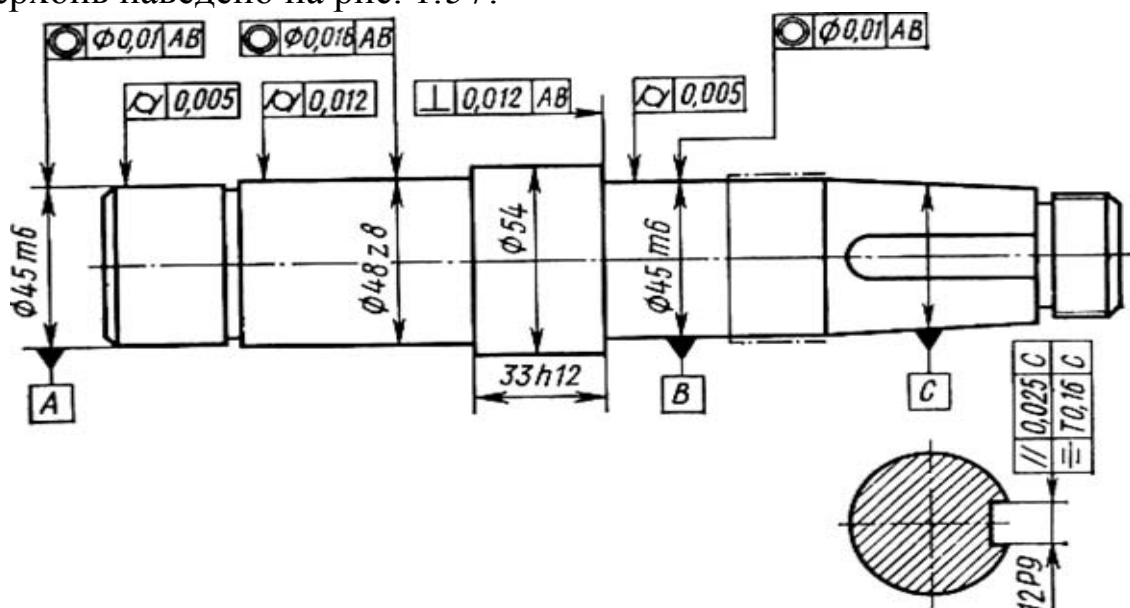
Допуски форми і розташування поверхонь вала
